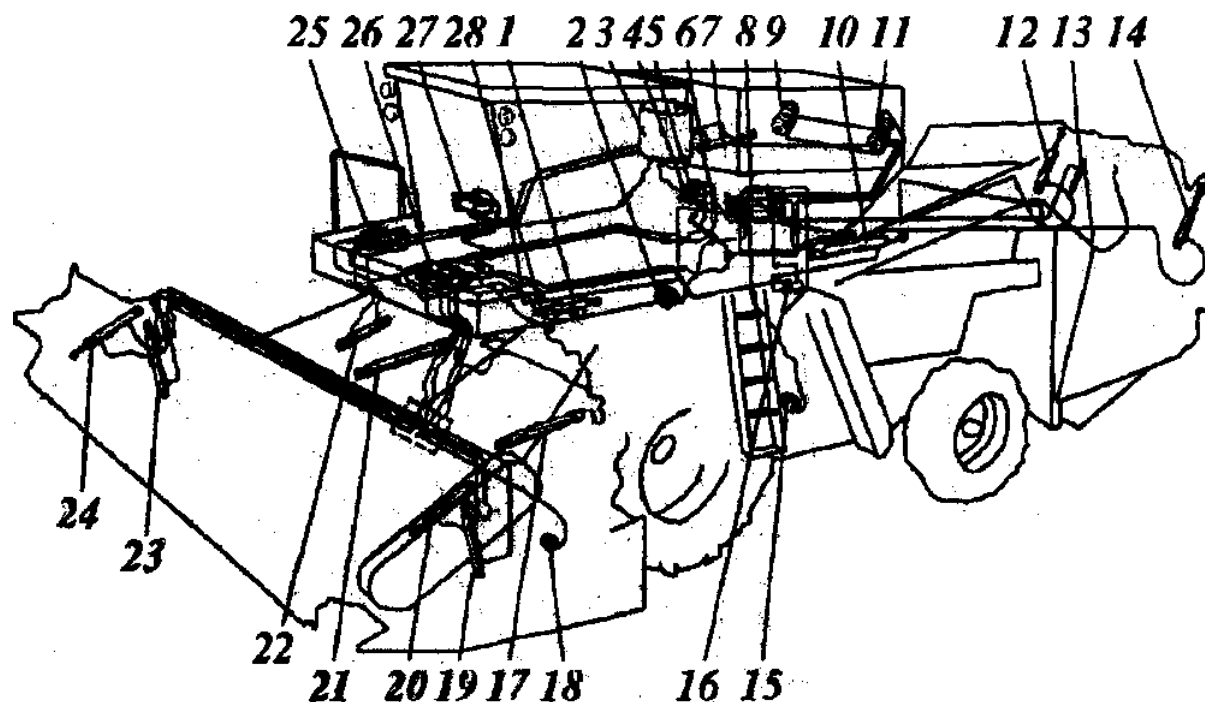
Схема основной гидросистемы комбайн: 1- гидроцилиндр включения молотилки ГА-93.000-10; 2- гидроцилиндр вариатора барабана РСМ-10.09.01.010А-03; 3-гидробак РСМ-ЮБ.09.09.360 (двигатель СМД-31А) или РСМ-10Б.09.69.010А (двигатели ЯМЗ-238АК и 740.12-210 КАМАЗ) или РСМ-10Б.09.69.010А-01 (двигатель Д461-51АМЗ); 4-полумуфта наружная Н036.67.100-10; 5- клапан напорный КН50.12,5; 6- гидроклапан с электромагнитным управлением КЭ1,6-2,5-16-01; 7- гидроцилиндр включения выгрузного шнека ГА-93.000-06; 8- электрогидрораспределитель 4РЭ50-29; 9Д1- вибраторы ГА-40.000В; 10- гидроцилиндр поворота выгрузного шнека ГЦ 63.500.16.000; 12,14- гидроцилиндр закрытия копнителя 54-9-145-06; 13- гидроцилиндр открытия защелки копнителя ГА 66.010А-03; 15- гидроцилиндр вариатора вентилятора очистки ЦС 83.000А; 16- распределитель копнителя РК 00.000-06; 17- гидроцилиндр вариатора мотовила ГА 83.000А; 18- гидроцилиндр подъема жатки РСМ-10.09.02.100Б; 19- гидроцилиндр вертикального перемещения мотовила ГА 81.000-08; 20- гидроцилиндр горизонтального перемещения мотовила ГЦС 32.180.16.000А или ЦГС 32.16.000-02; 22-гидроцилиндр прокрутки жатки ГА-93.000-08; 23-гидроцилиндр вертикального перемещения мотовила ГА 80.000-03; 24-гидроцилиндр горизонтального перемещения мотовила ГЦ40.180.16.000А или ЦГ 40.16.000-02; 25- электрогидрораспределитель 2РЭ50-00; 26- электрогидрораспределитель 5РЭ50-44; 27- насос НШ-32А-3 (двигатель СМД-31А) или НШ-32М-4 (двигатель ЯМЗ-238АК) или НШ-32А-3-Л (двигатель Д461-51АМЗ) или НШ-32У-3 (двигатель 740.12-210 КАМАЗ); 28- клапан дросселирующий настраиваемый КДН 00.000-06
